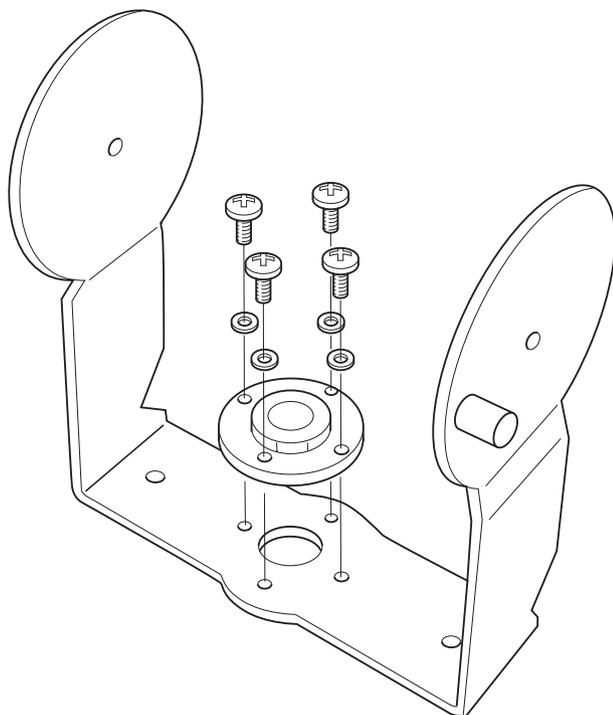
Fixation de la plaque au support de suspension en cas de fixation au mur
